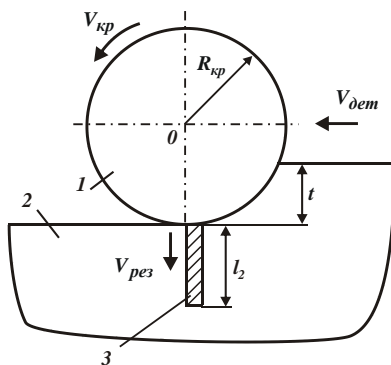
Расчетная схема параметров процесса плоского шлифования: 1 – шлифовальный круг; 2 – обрабатываемая деталь; 3 – адиабатический стержень
